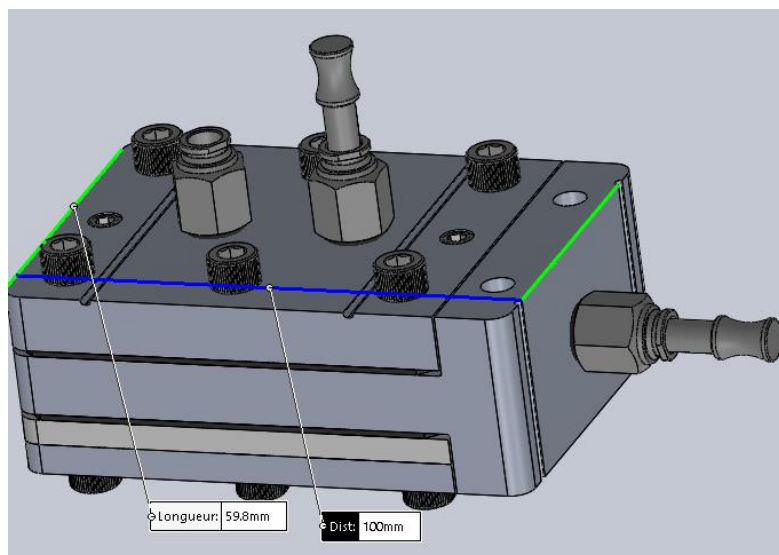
Vue d'ensemble CAO du moule complet, monté pour une injection par la face fine
